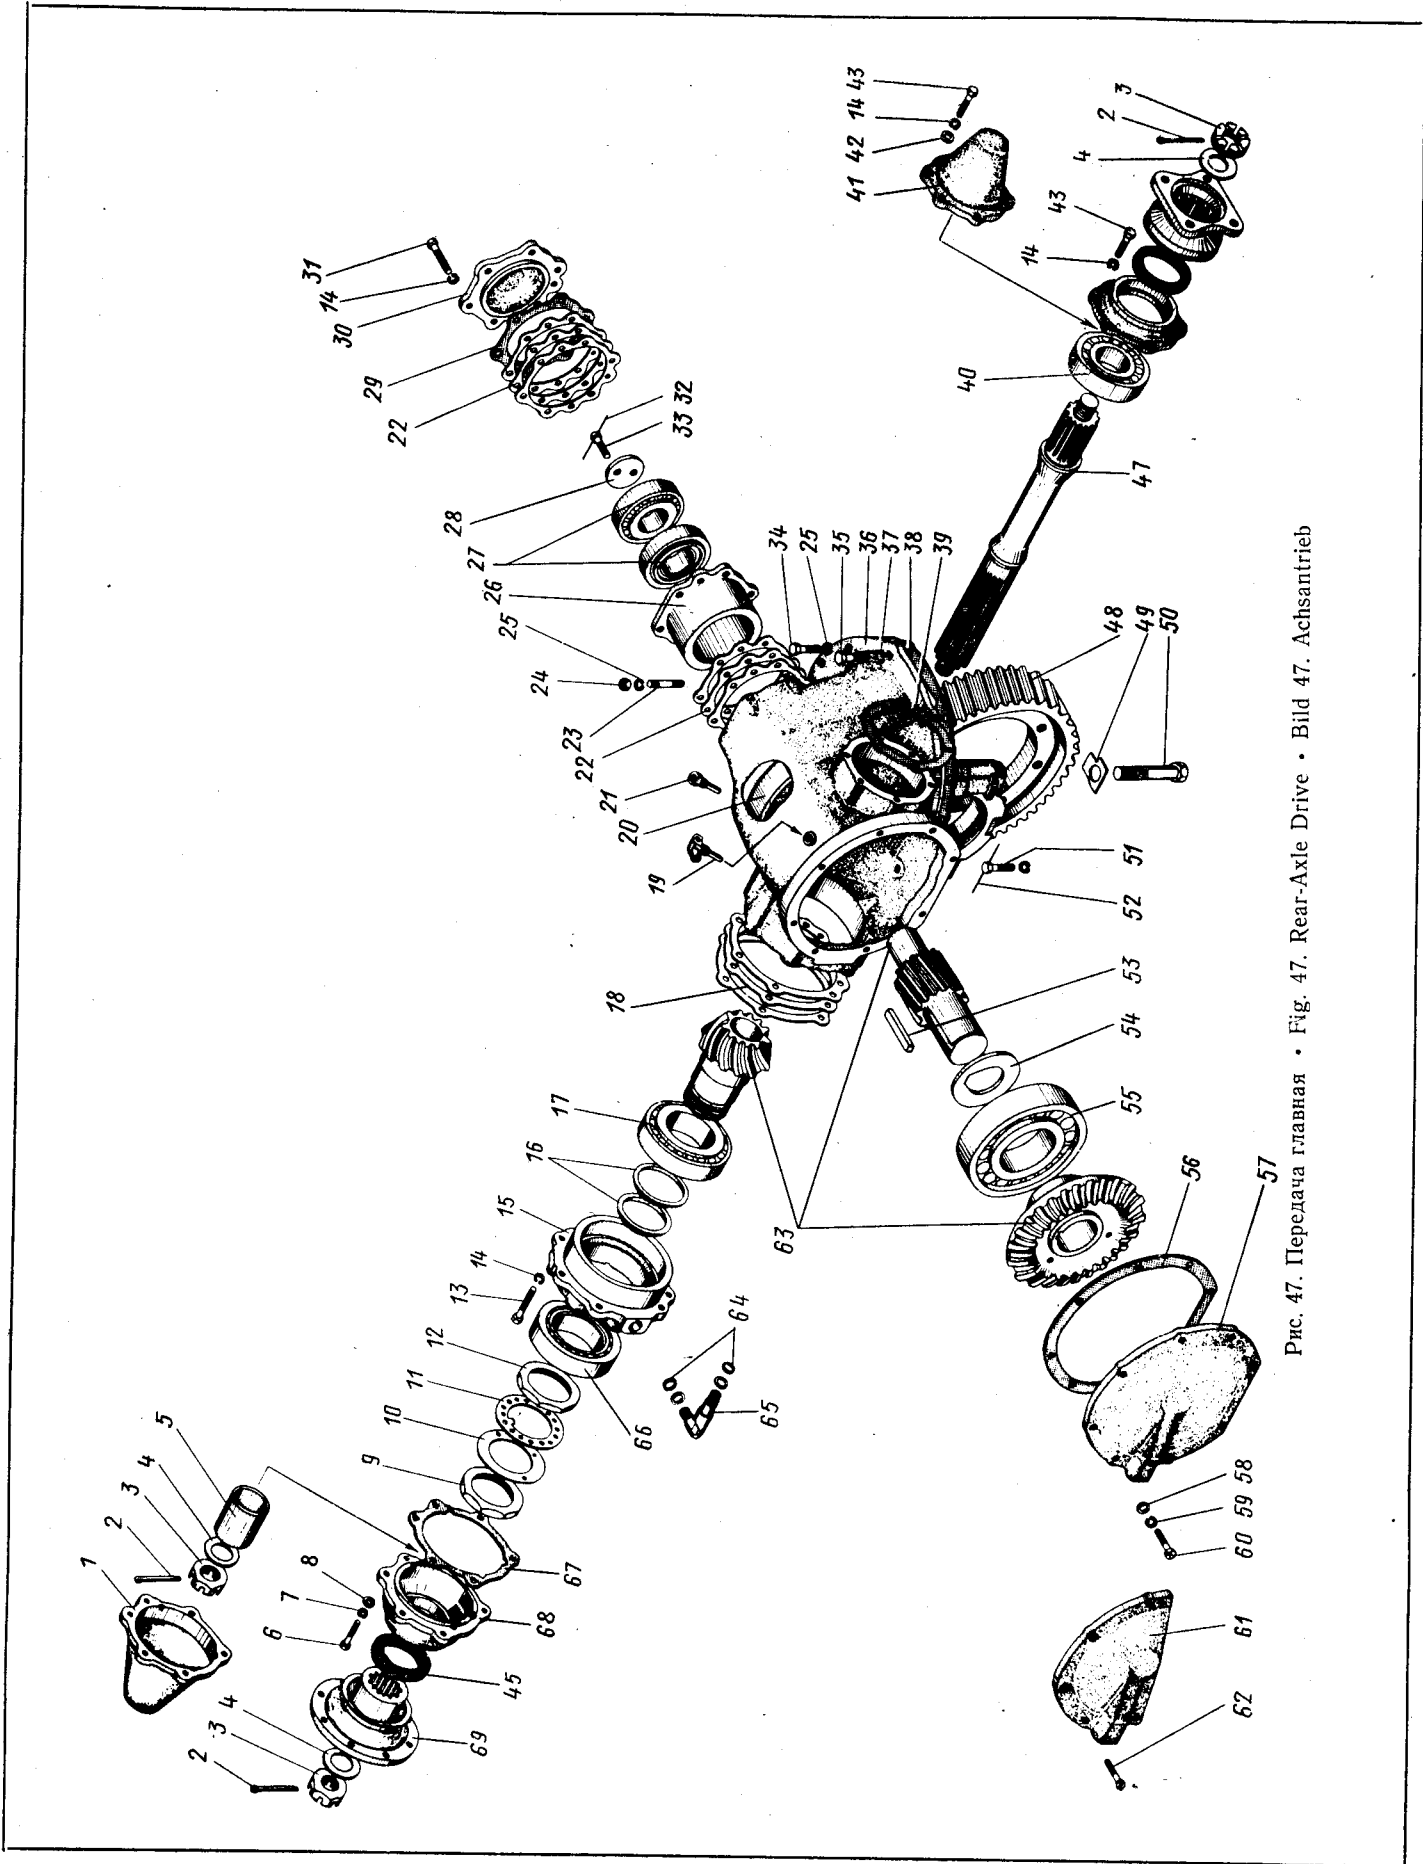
Передача главная • Fig. 47. Rear-Axle Drive • Bild 47. Achsantrieb
